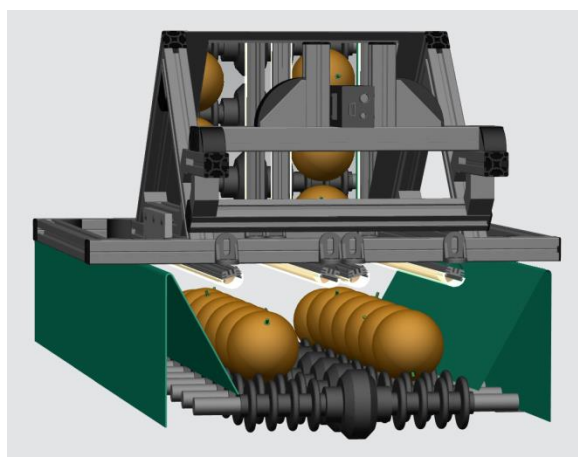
Diseño del sistema de visión sobre una línea de rodillos
